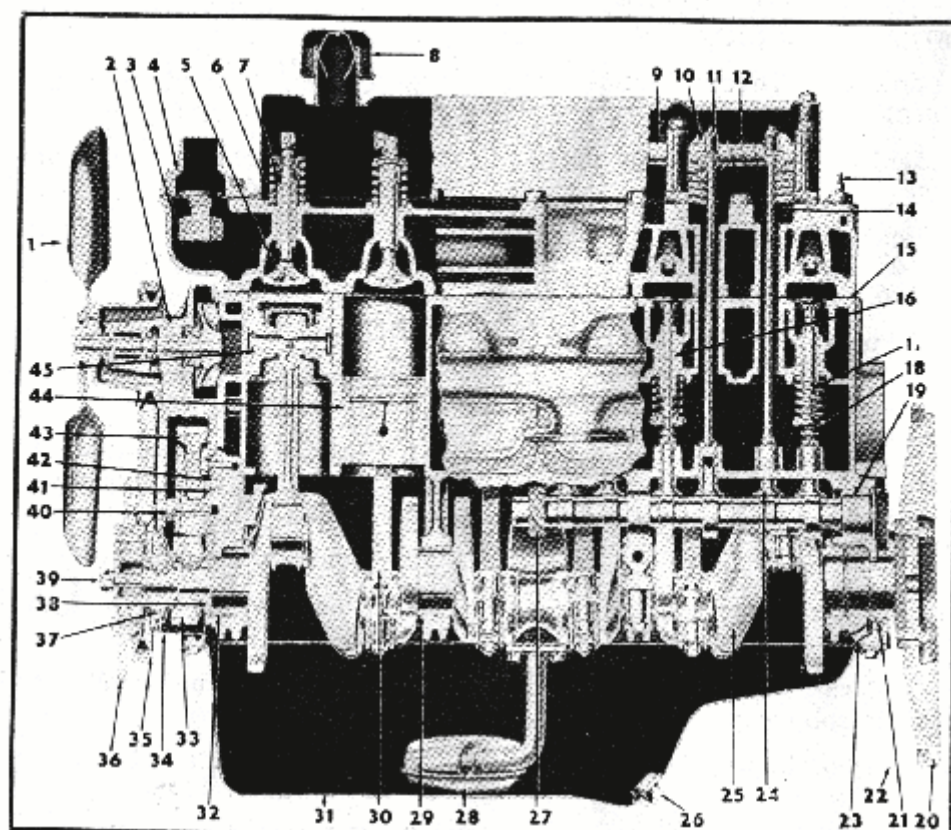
CORTE VERTICAL DO MOTOR, VISTO DE LADO
